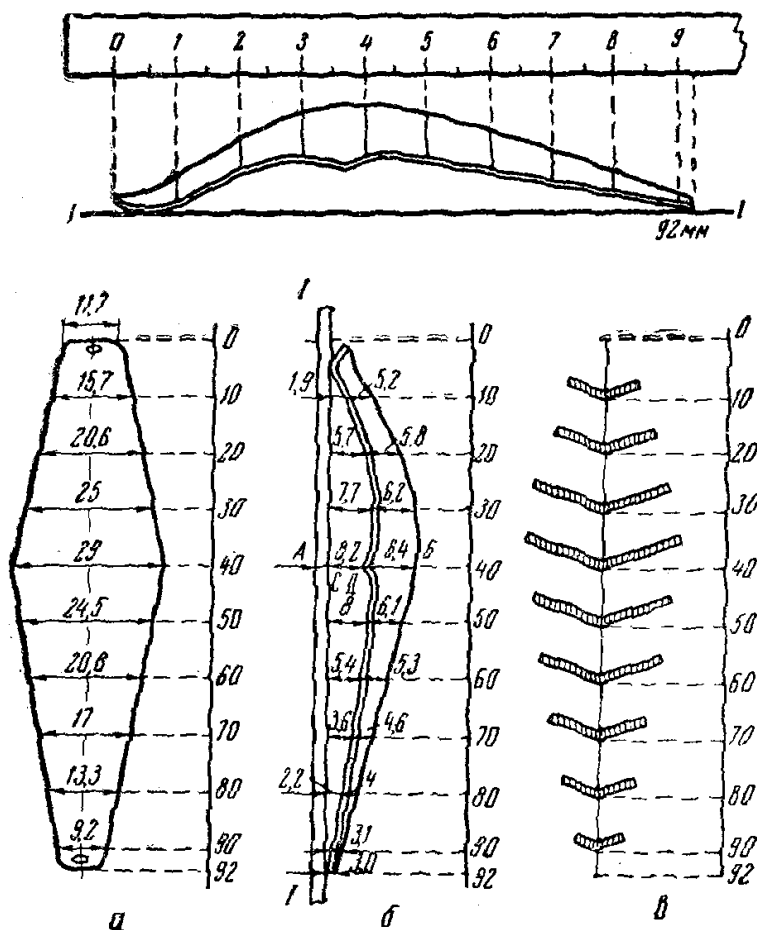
Порядок изготовления блесны «Кольской» (вверху — разметка образца).
